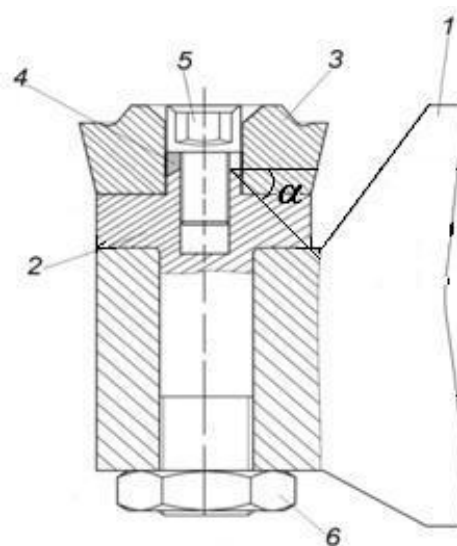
Усовершенствованная конструкция сборного чашечного резца
